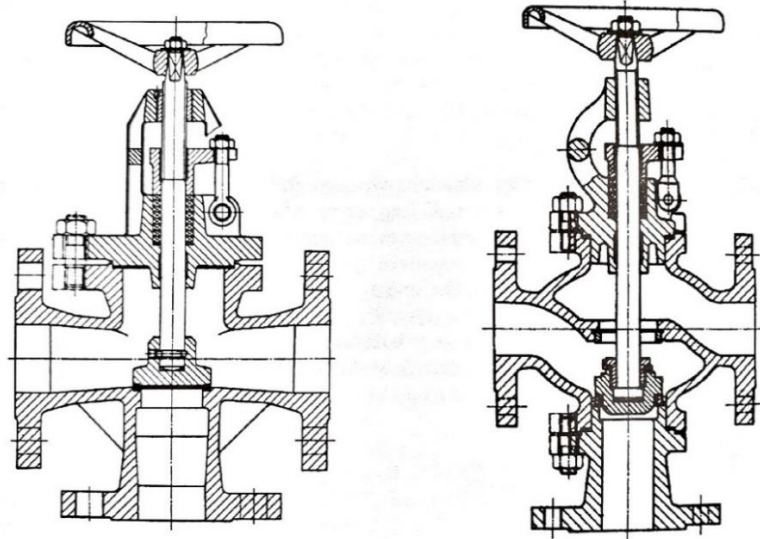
Stavební délky armatur; a) – uzavírací ventil;
